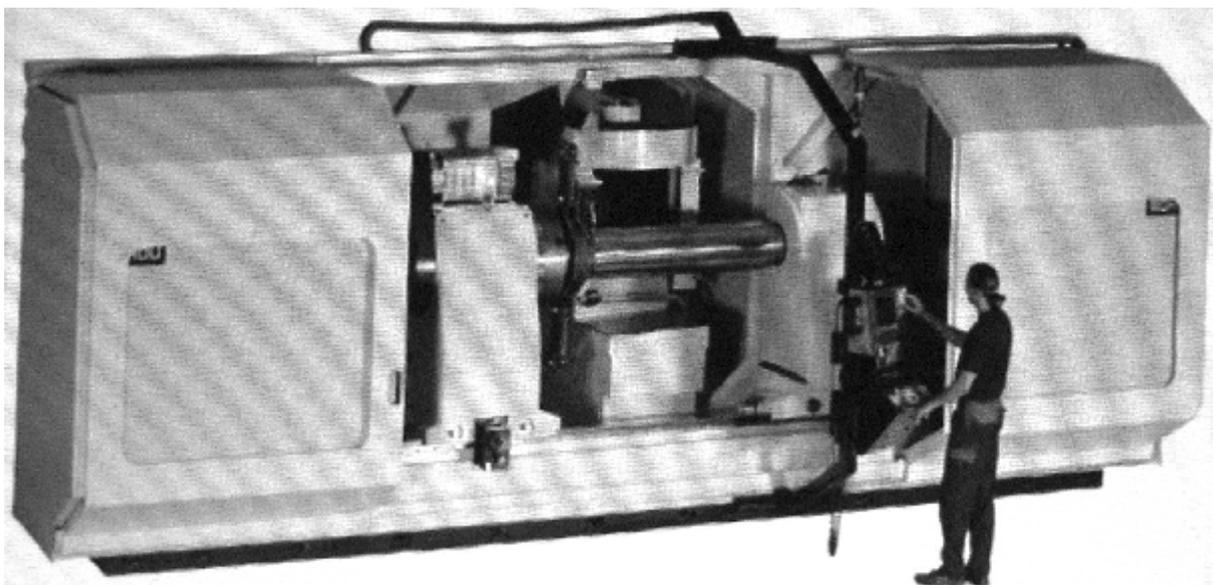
Уникальный тяжелый обрабатывающий центр с ЧПУ для врезного и цилиндрического шлифования типа CNC – В; угловая точность расположения бабки – 0,0001 град.
